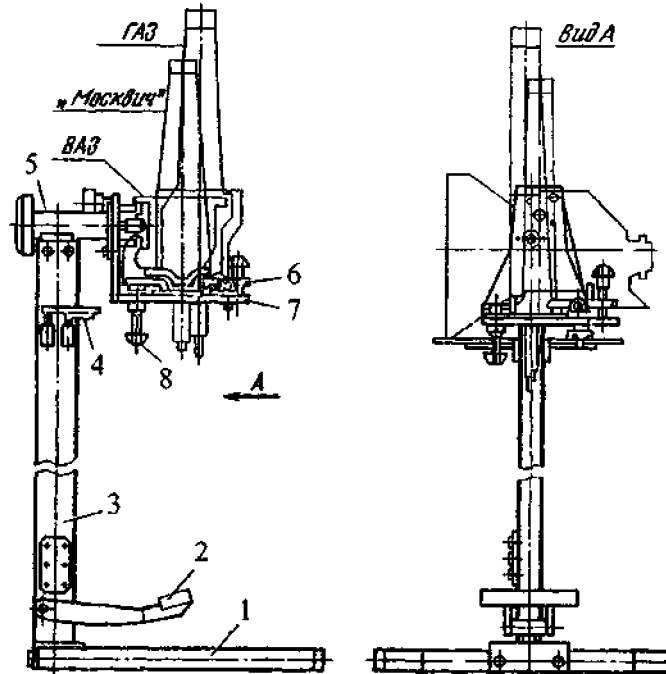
Стенд Р-278М для разборки и сборки коробки передач
